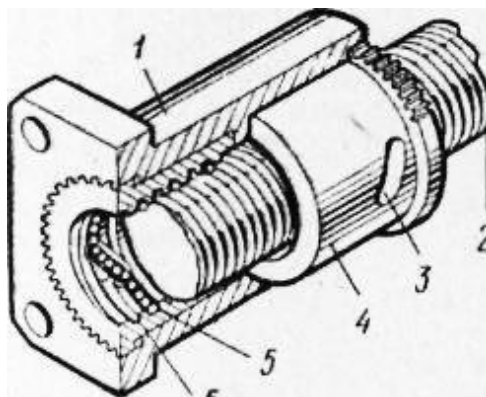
Схема кулько-гвинтова передача токарного верстата
